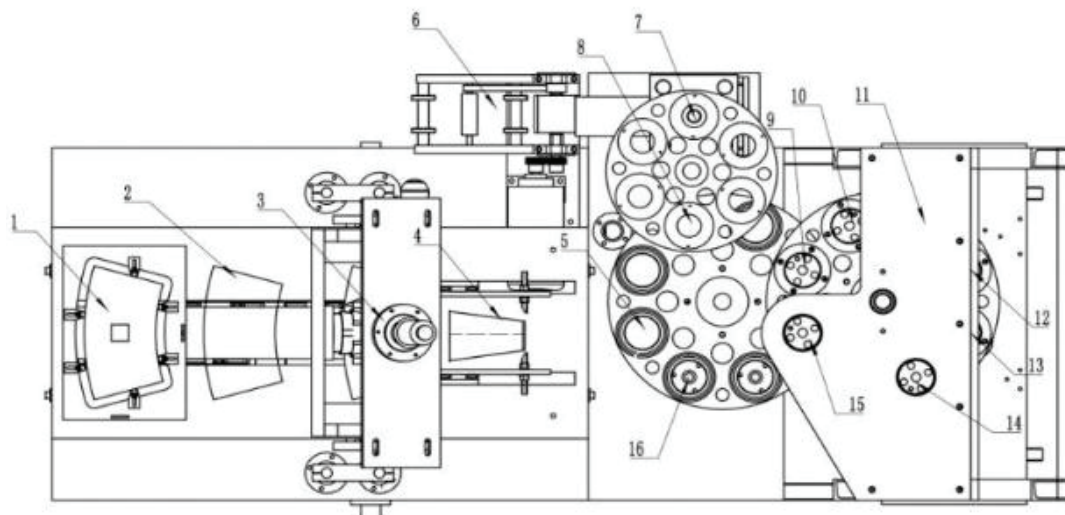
Общий вид автоматизированного комплекса (вид сверху)
